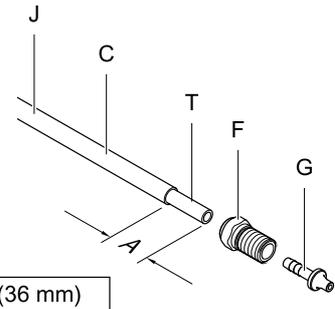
Abmessungen an Pistole für ungeschirmten Schlauch 24M733
